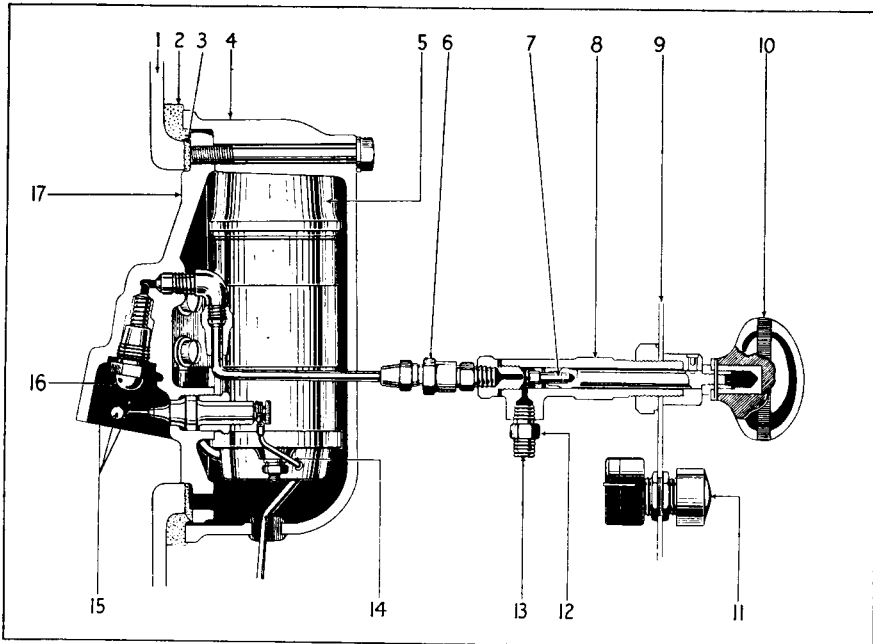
а. Запальное приспособление (типа форсунки) для воздушного обогревателя.
